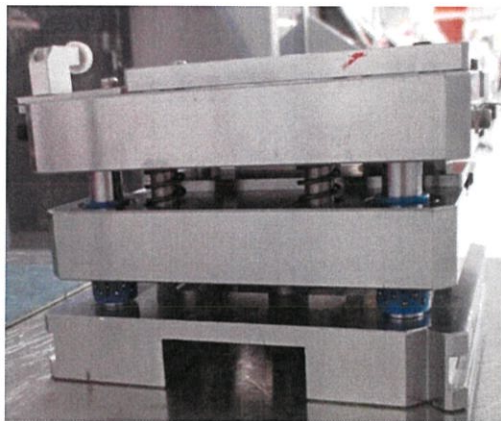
แสดงส่วนประกอบทั้งหมดของเครื่องมือ Cutting Tool
